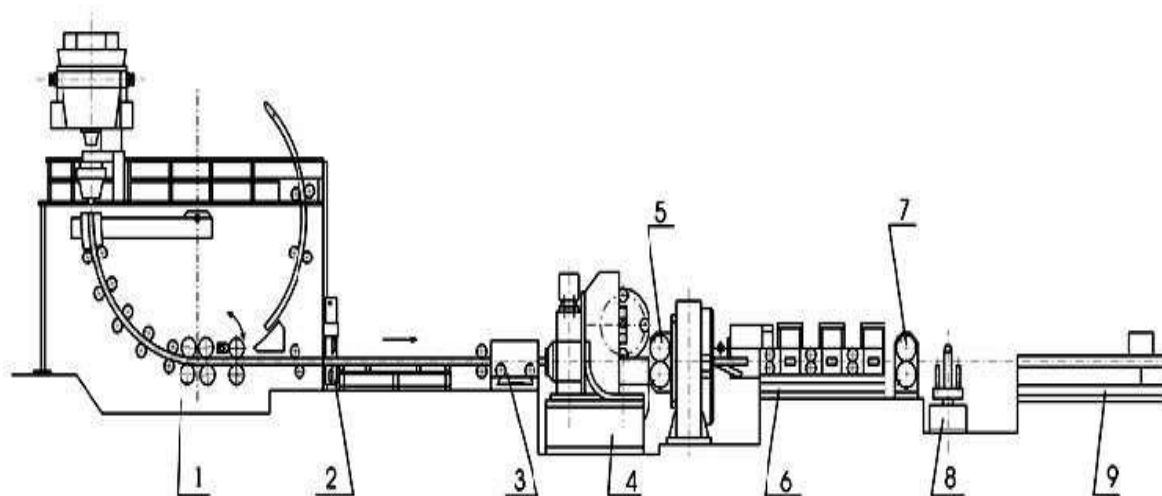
Схема розташування ливарно-прокатного агрегату з планетарним станом для сортового прокату та катанки: 1 - однорівчачова МБРС; 2 - маятникові летючі ножиці; 3 - індукційне підігрівне устаткування; 4 - сортовий планетарний стан; 5 - летючі ножиці для обрізання металу; 6 - група клітей поздовжнього прокатування; 7 - барабанні летючі ножиці для обрізання під час руху матеріалу; 8 - моталки для змотування дроту; 9 - устаткування для прибирання бунтів.
